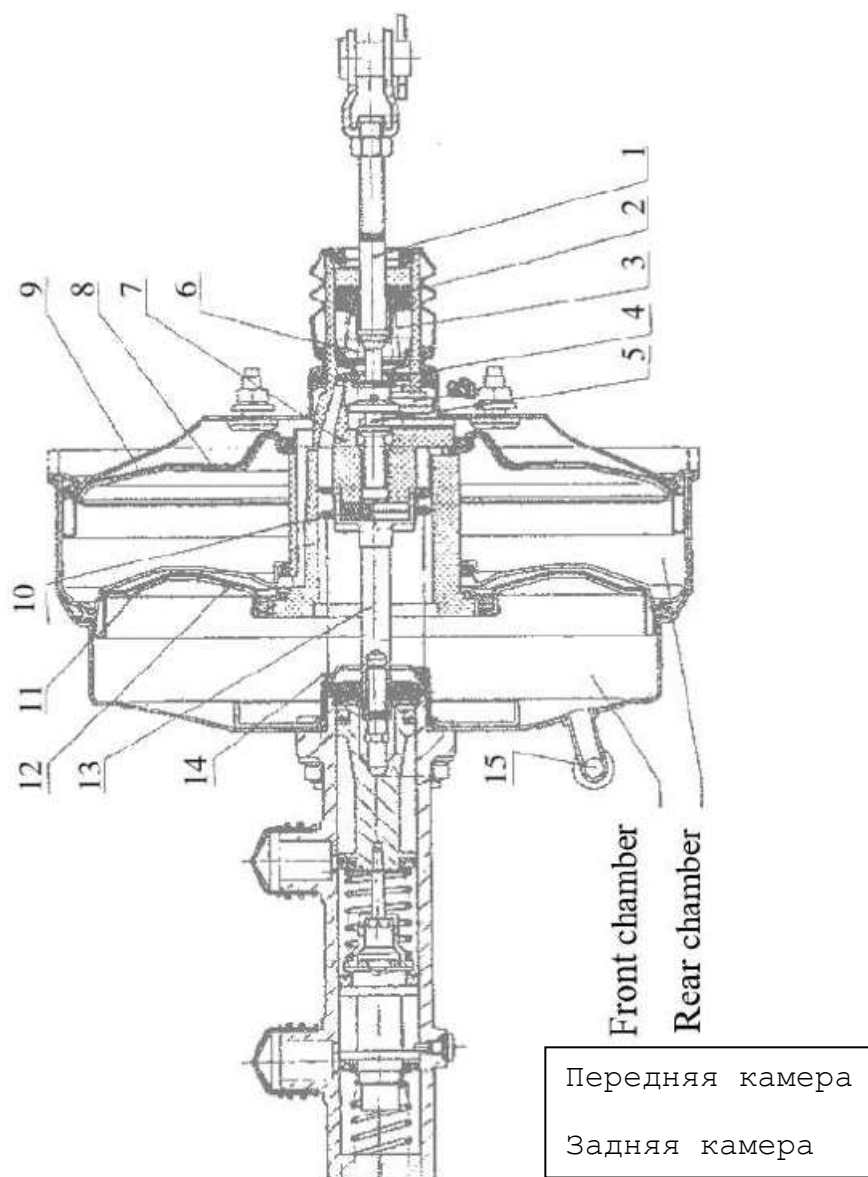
Конструктивная схема вакуумного усилителя и главного тормозного цилиндра:
